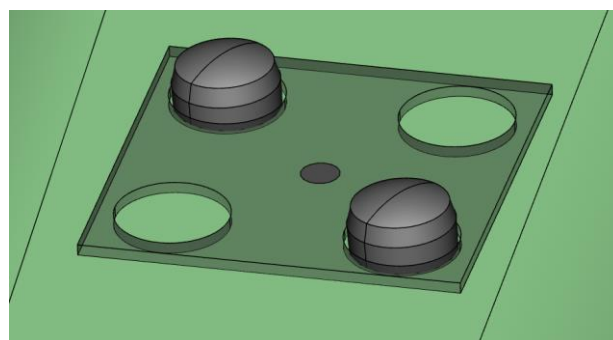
Metallplatte, welche über Stifte und Magnet im Werkzeug fixiert ist
